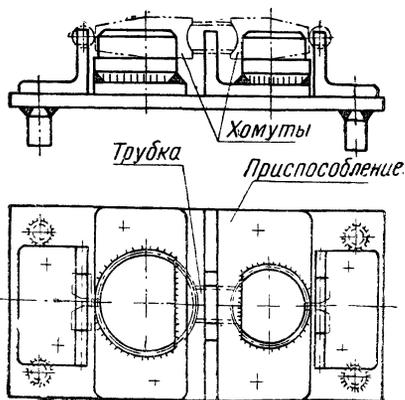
Приспособление для сборки и прихватки кронштейна.
